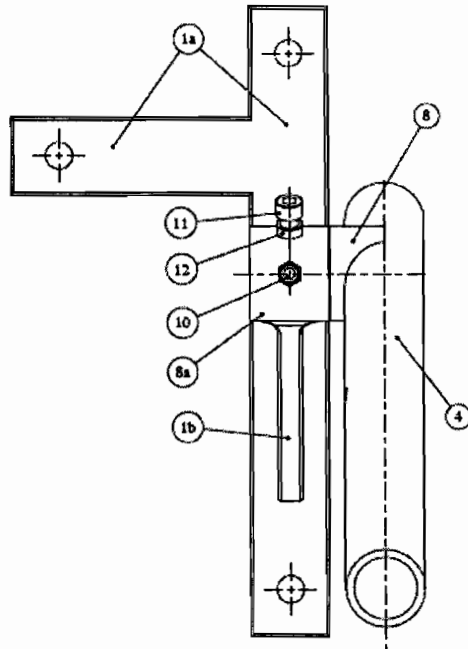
Componente suport de fixare și lagăr; prinderea lagărului de maneta principală, vedere de sus
